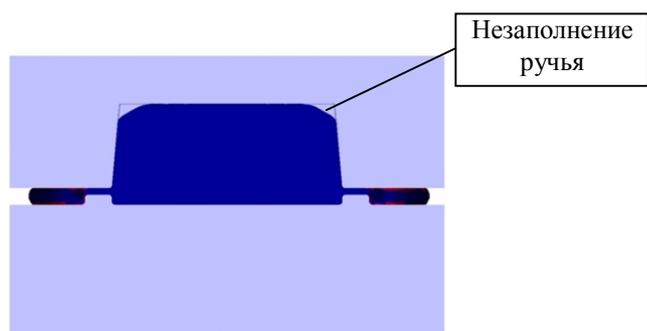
Результат штамповки с заготовкой круглого поперечного сечения
